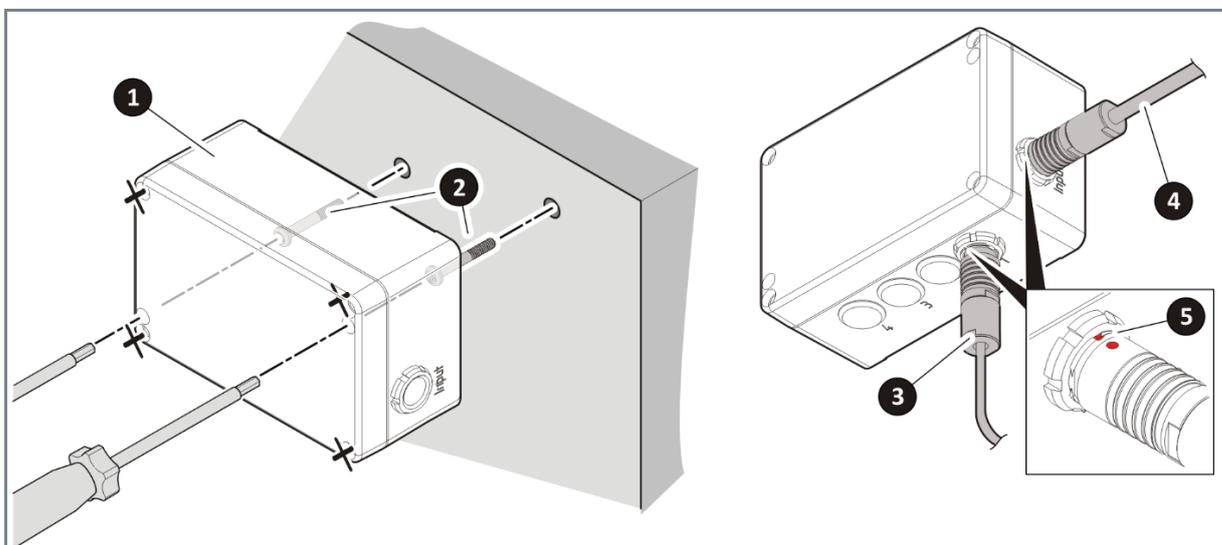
DynamicMold® Controller installieren und Stecker verbinden
